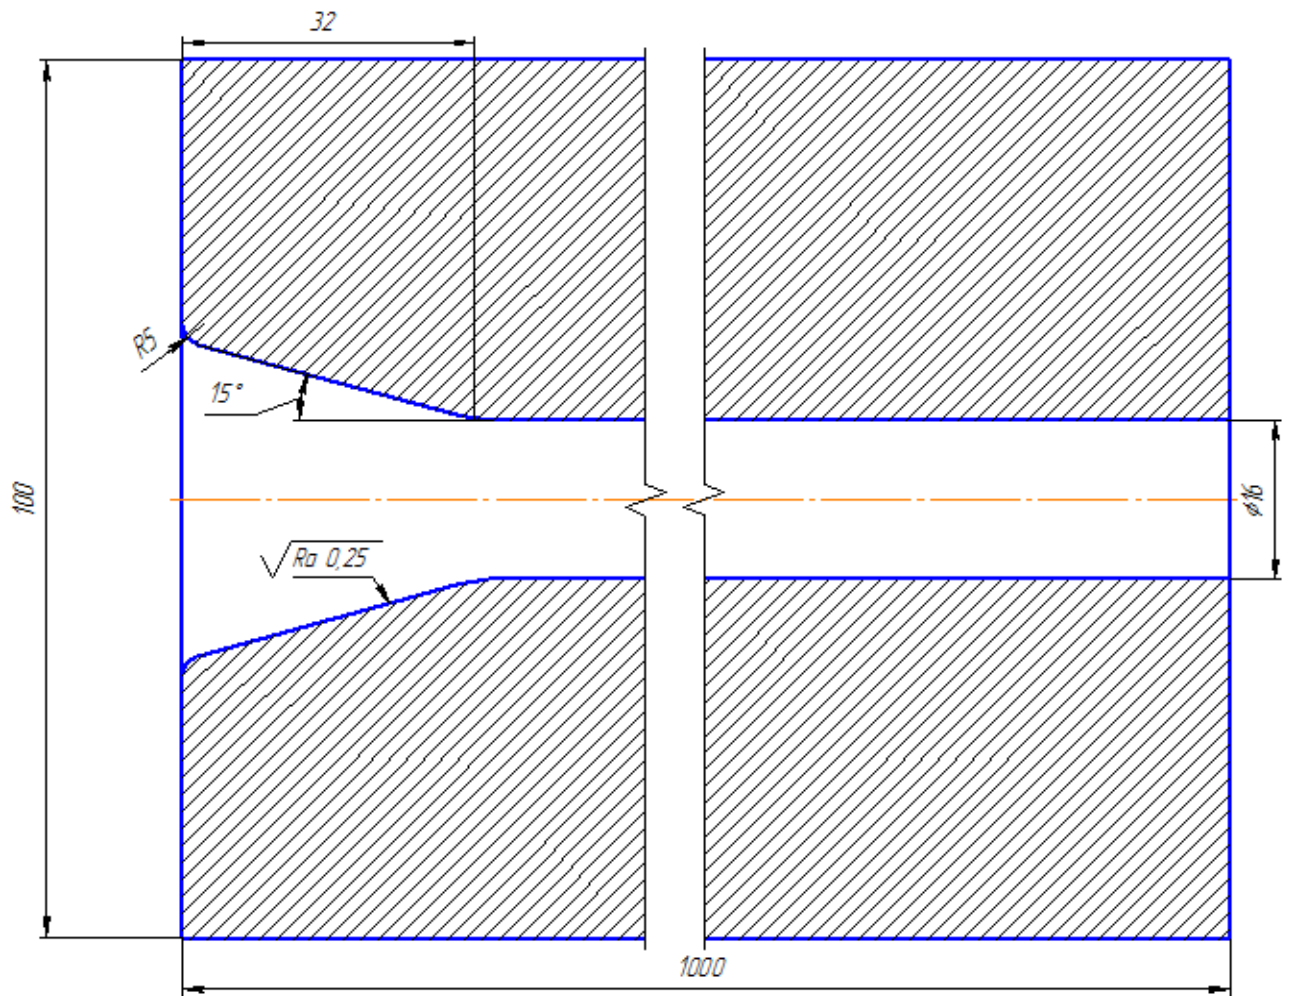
Конструкция фильеры (продольный разрез)
